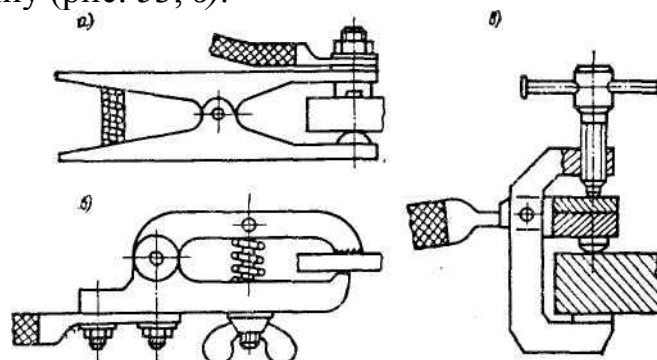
Неподвижные зажимы обратного провода: а — пружинный; б — винтовой; в — винтовая трубка
